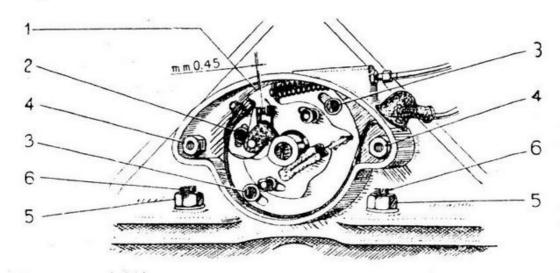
Regolazione contatti ruttore: 1) Contatto fisso - 2) Vite bloccaggio contatto fisso - 3) Viti per fissaggio e messa a punto ruttore - 4) Dadi a colonnetta fissaggio scatola ruttore - 5) Dadi fissaggio testa - 6) Colonnette fissaggio testa.
